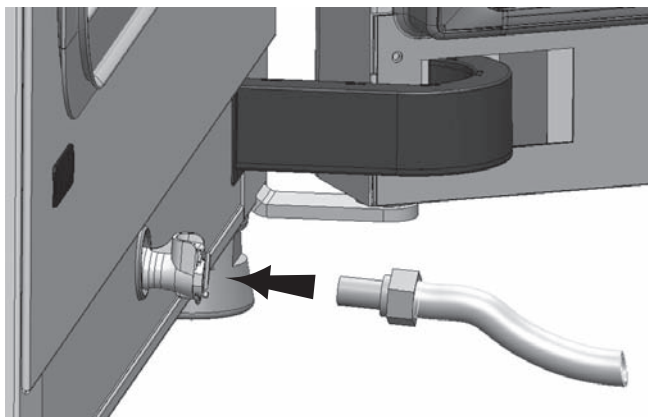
Дренажно-заправочный клапан резервуара для воды
